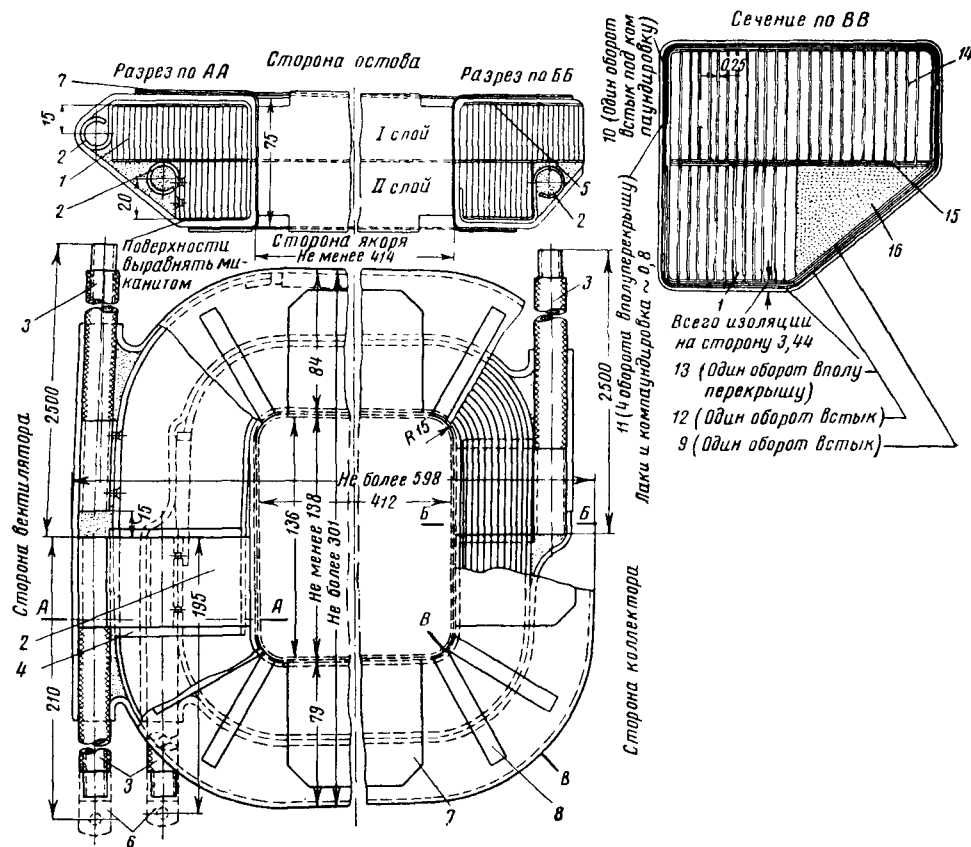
Обмотка якоря тяговых двигателей типов ДМП-151 и ДМП-150
